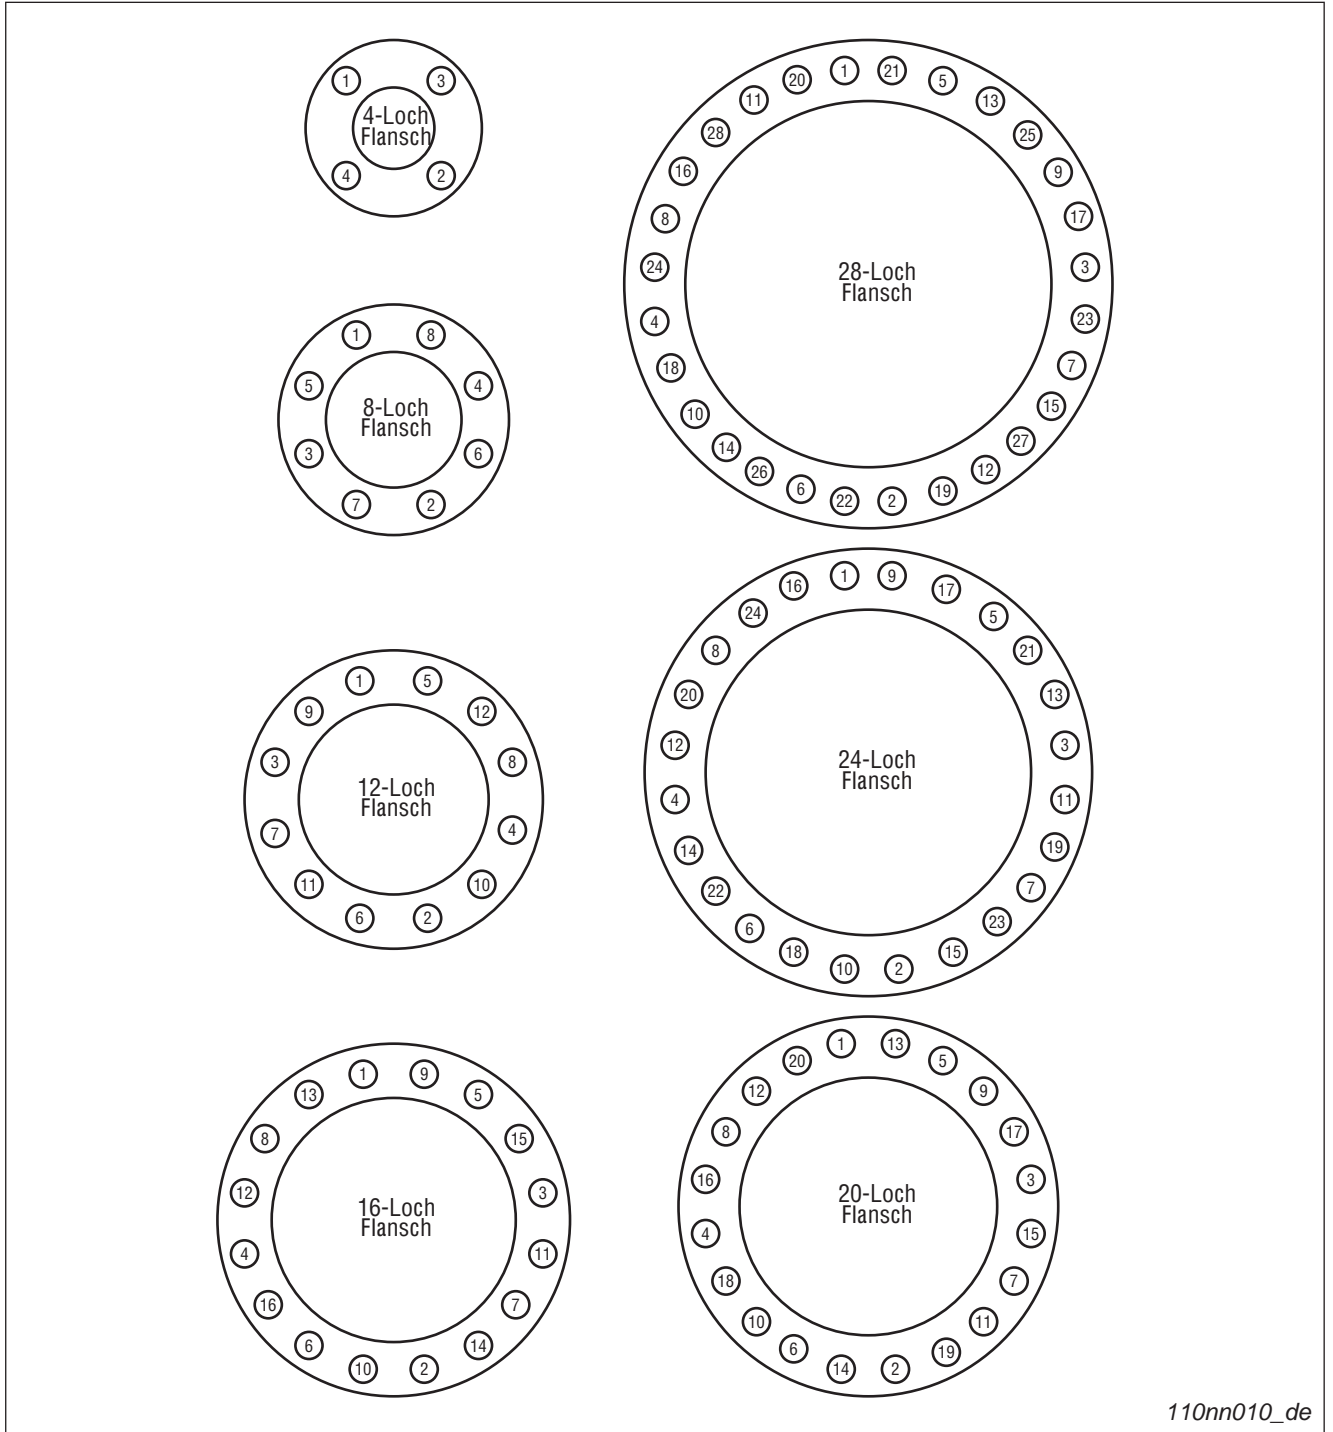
Anziehreihenfolge für Flanschschrauben
